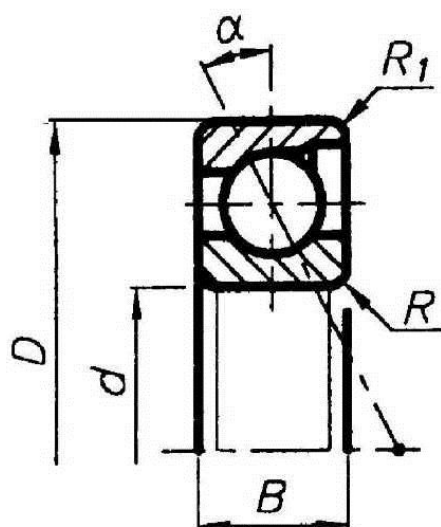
Габаритные размеры шариковых радиально-упорных подшипников
